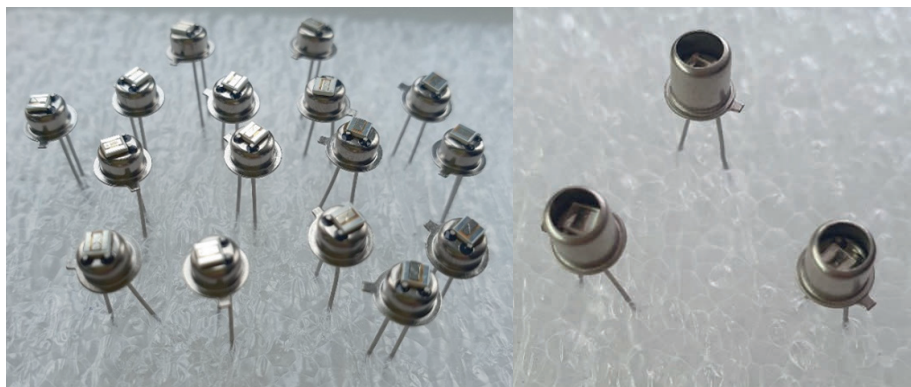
Воспламенитель в корпусе без колпачка и с приваренным колпачком
